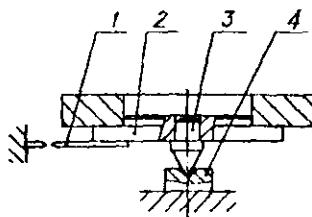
2. Схема весов для статической балансировки деталей: 1-стрелки; 2-площадка; 3-острие; 4-опора.
